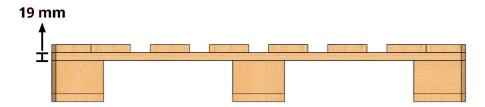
Esquema de vista lateral de um pallet com tábuas de ligação com 19 mm de espessura.
